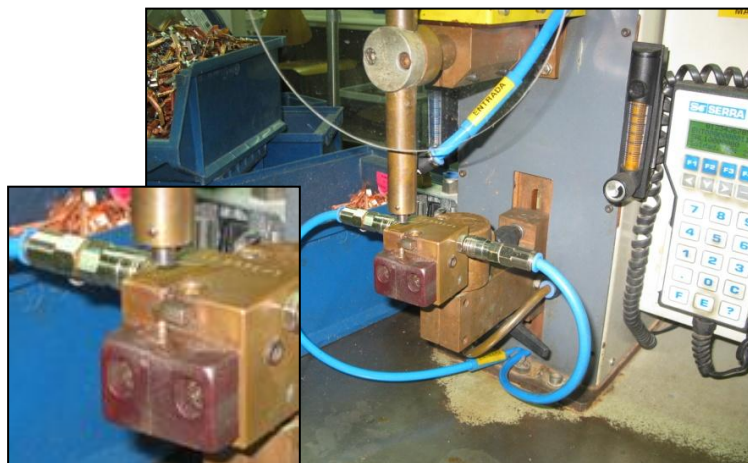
Cone de cobre e JIG numa máquina de soldadura. À esquerda evidenciam-se os eléctrodos superior e inferior.
